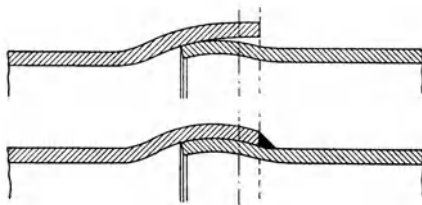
Kugelschweißmuffe 10° (Deutsche Röhrenwerke A. G., Düsseldorf).
